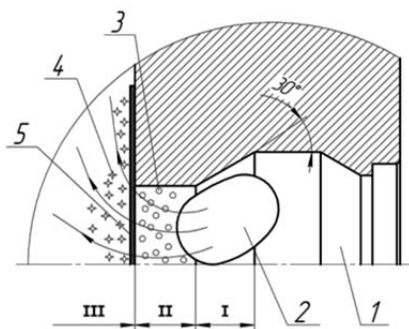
Схема механізму виникнення кавітаційного зношення в проточці донньої частини робочого циліндра:
